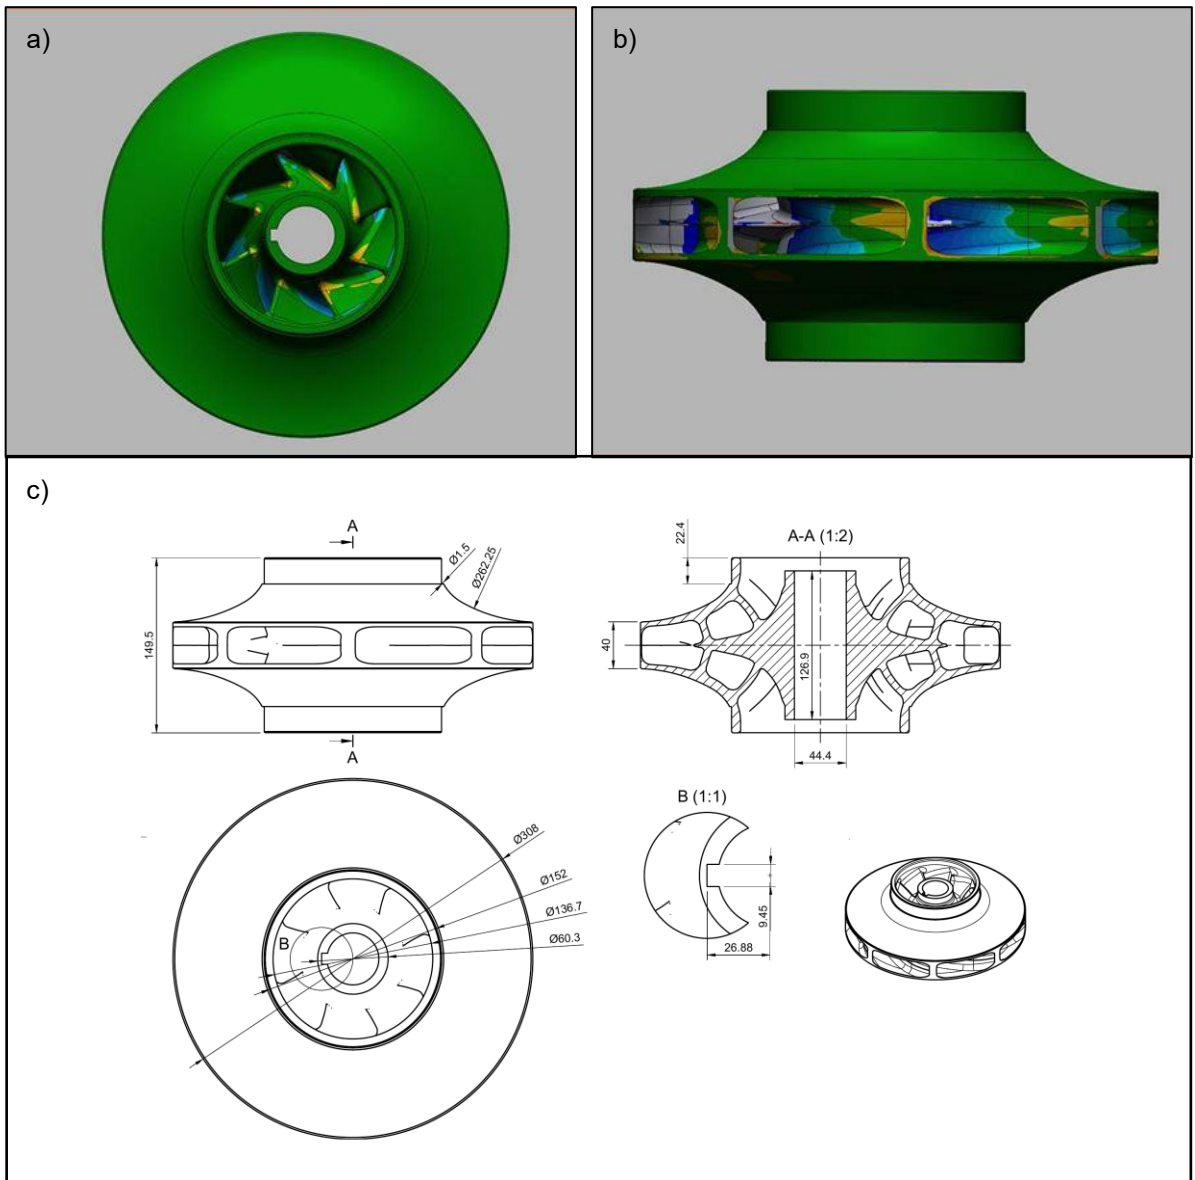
Modelo do rotor para estudo obtido pelo Scanner 3D Calibry Thor: (a) vista de topo a 3D; (b) vista lateral a 3D; (c) dimensões geométricas da vista de tipo, lateral e em cortes.
